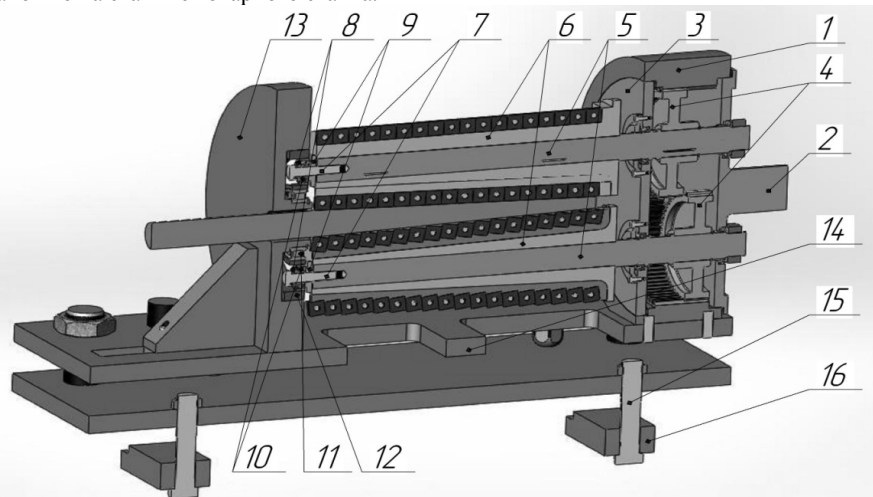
Устройство для обработки профильной части пружин совместно с устройством обеспечения жесткости
